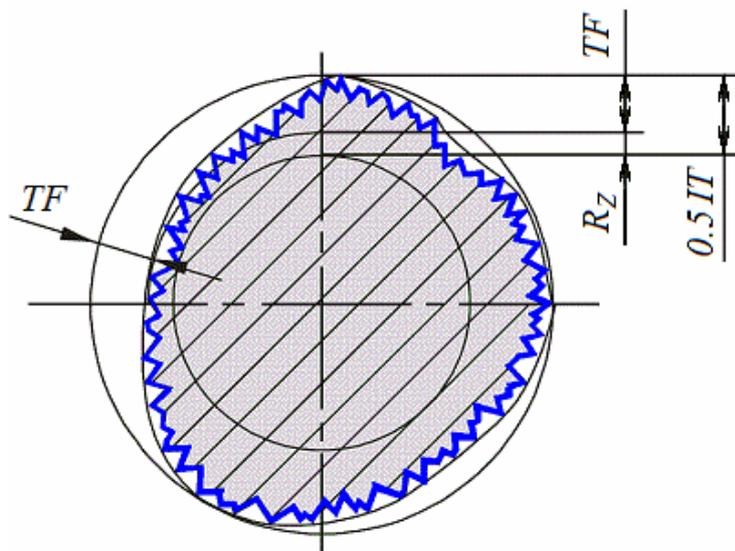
Связь между шероховатостью и допуском размера, формы и расположения поверхностей
